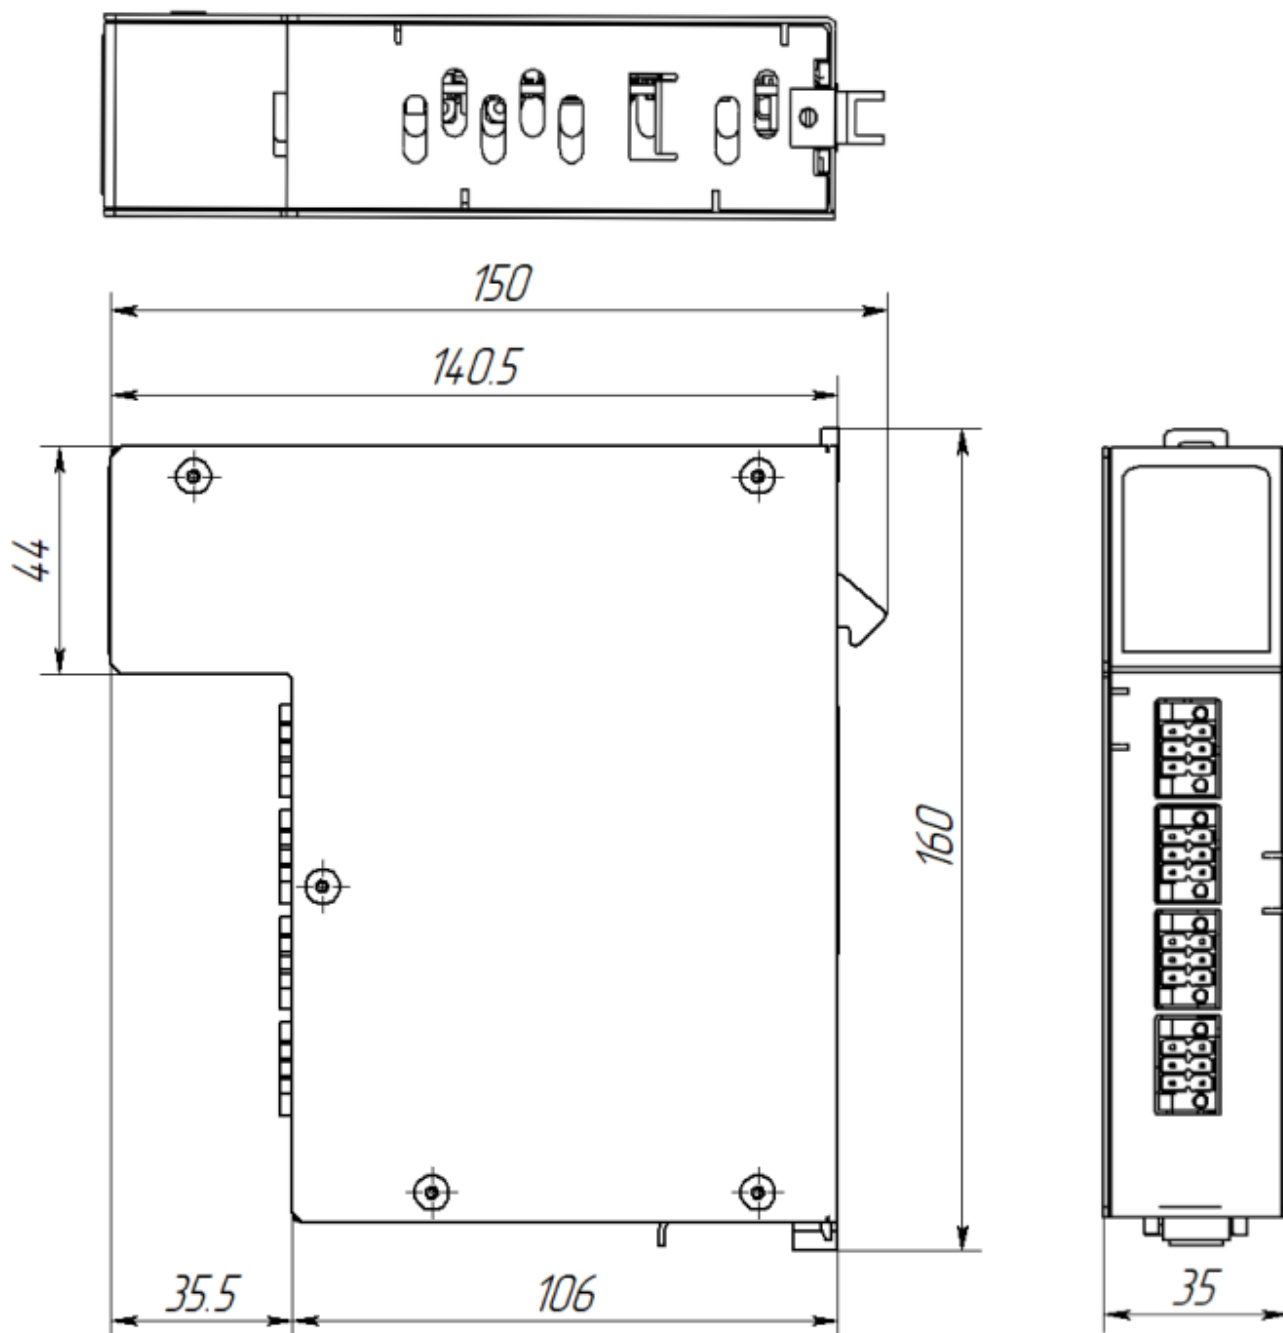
Габаритные и присоединительные размеры модуля коммуникационного с интерфейсом RS-232 в металлическом корпусе
